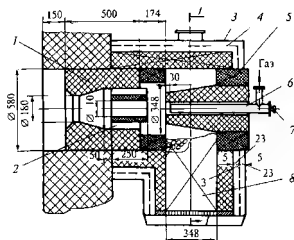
61 Регенеративный горелочный блок ВНИИМТ: 1 амбразура, 2 — форкамера, 3 кожух, 4 — перфорированная перегородка, 5 защитный камень, 6 — газовая фурма, 7 — запально-дежурная горелка; 8 — регенератор, 9 — дымовой патрубок; 10 — воздушный патрубок
